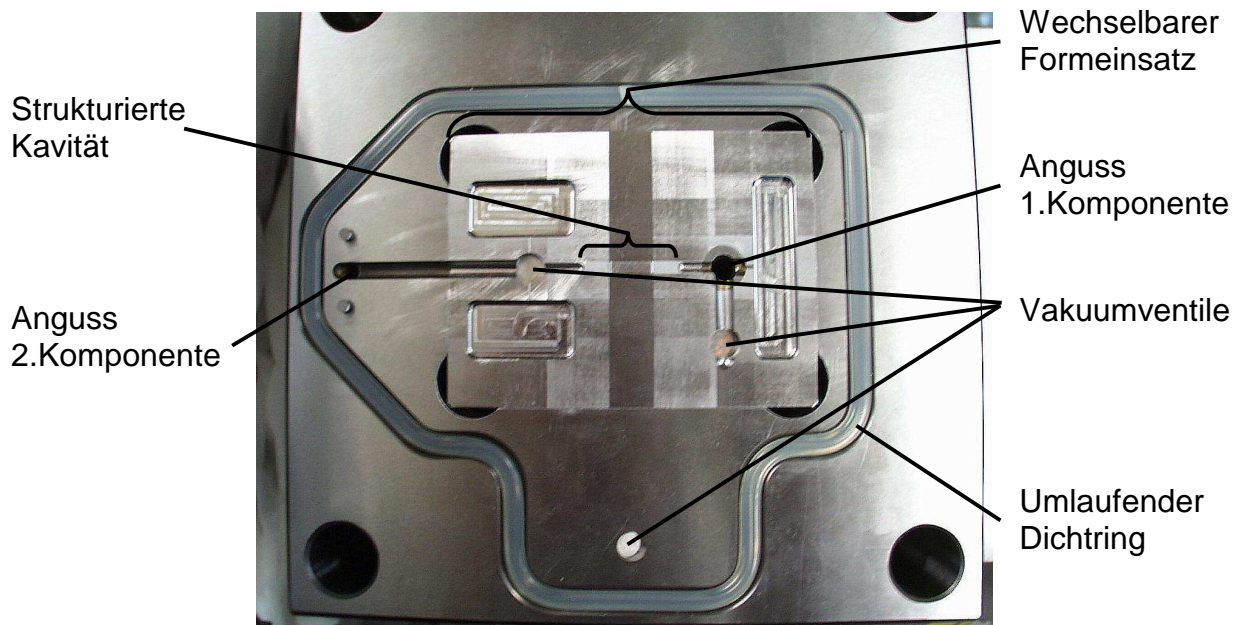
2K-PIM-Werkzeug mit Formeinsatz Zugstab (Düsenseite)
